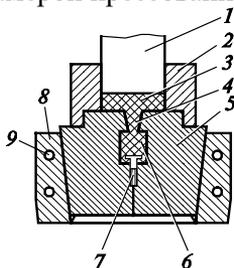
Рабочая часть пресс-формы для литьевого прессования с верхней камерой прессования:
